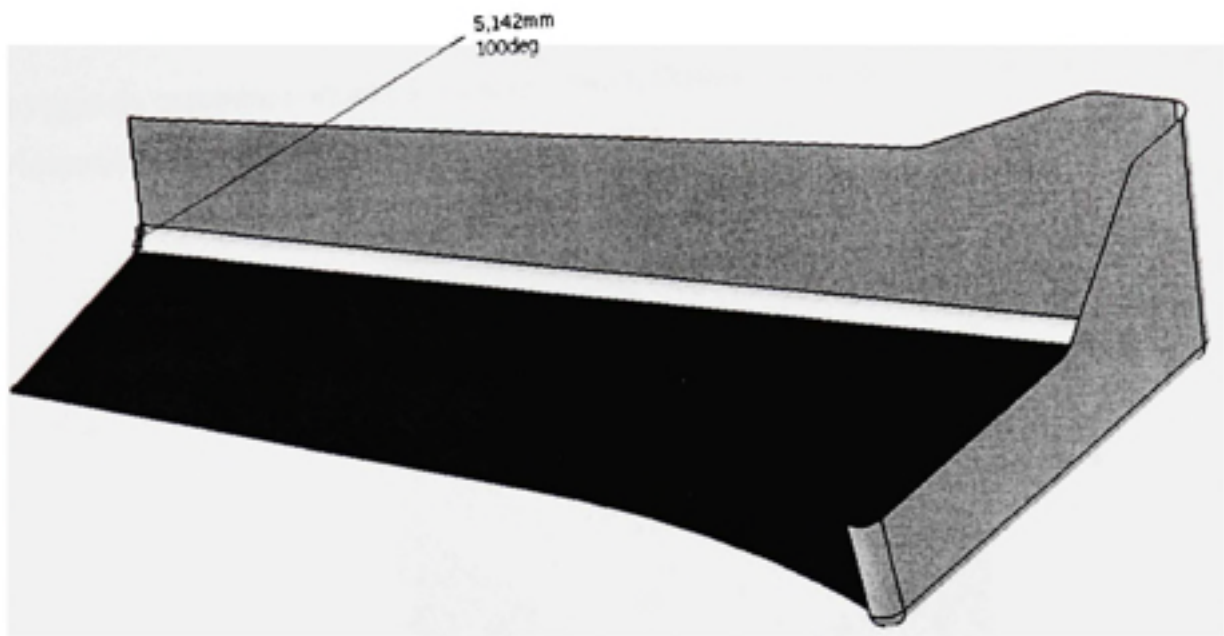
Dimension relative - Angle entre un flanc et la surface de fond
